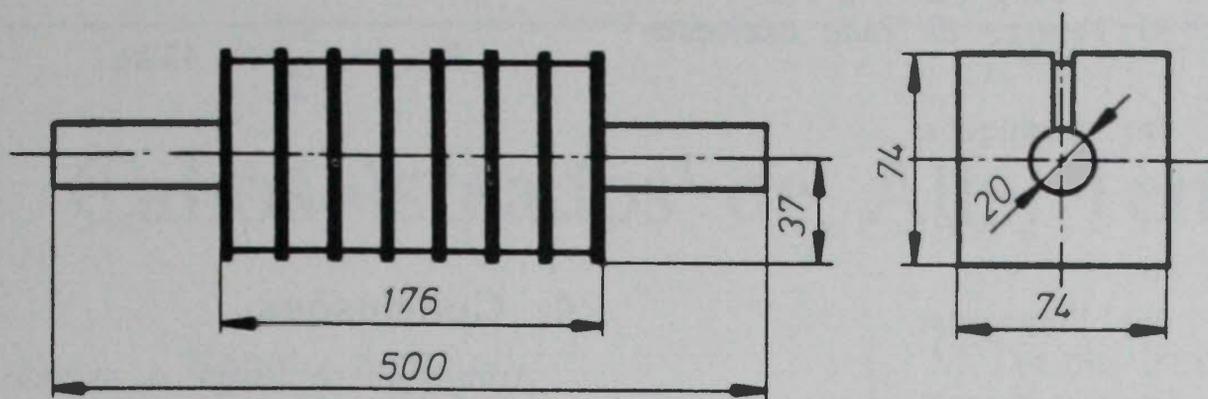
Dimensões características de um protótipo de um motor linear de indução tubular
